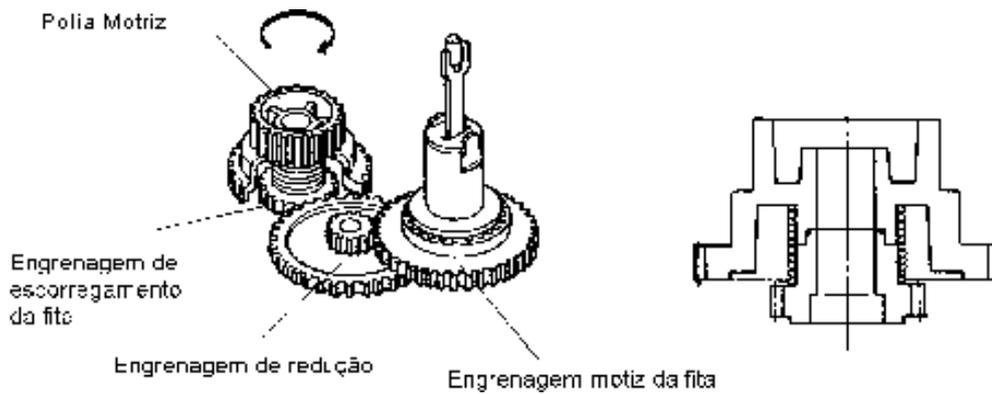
Cadeia de Engrenagens do Avanço de Fita
